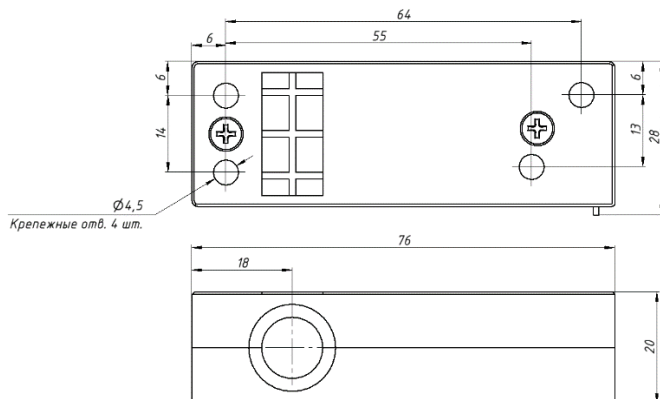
Габаритные и установочные размеры замка Promix-SM.420.10
